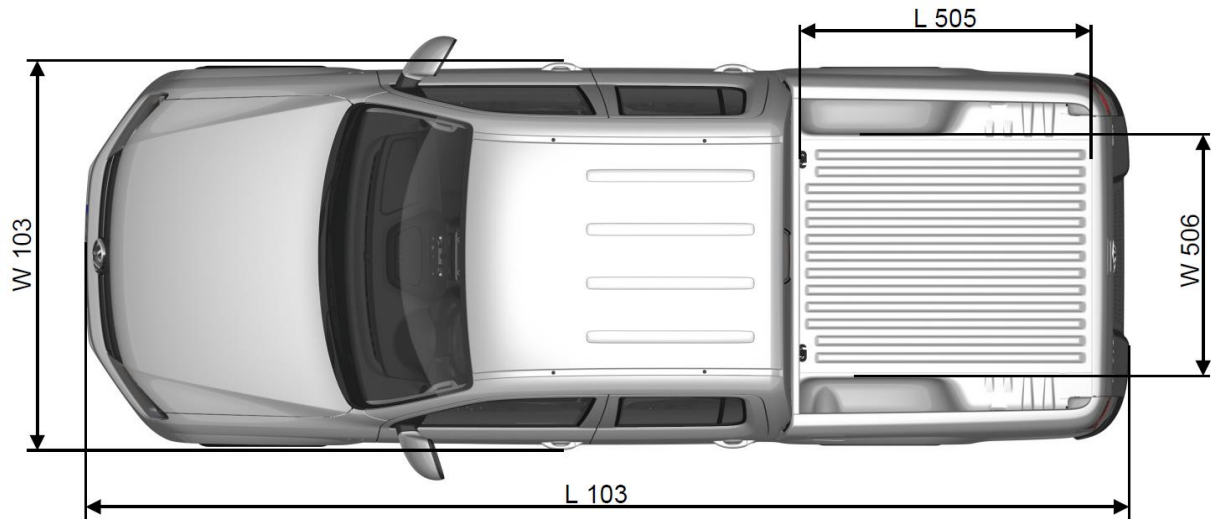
Draufsicht Amarok-DC (Double Cab)
